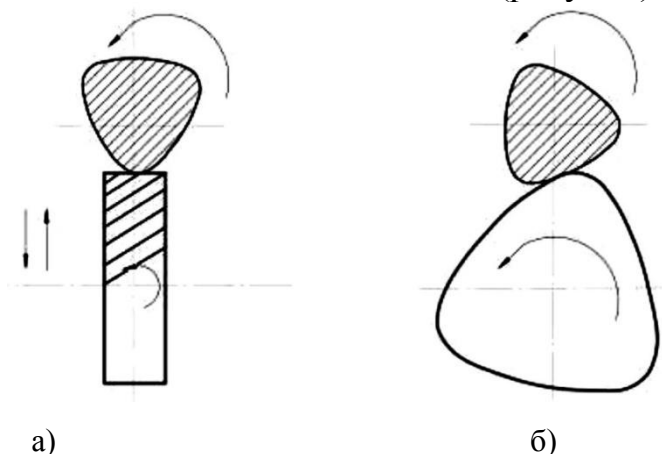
Способи обробки валів із рівноосним контуром: а – периферією циліндричної фрези; б – дисковою фрезою із радіальною подачею
